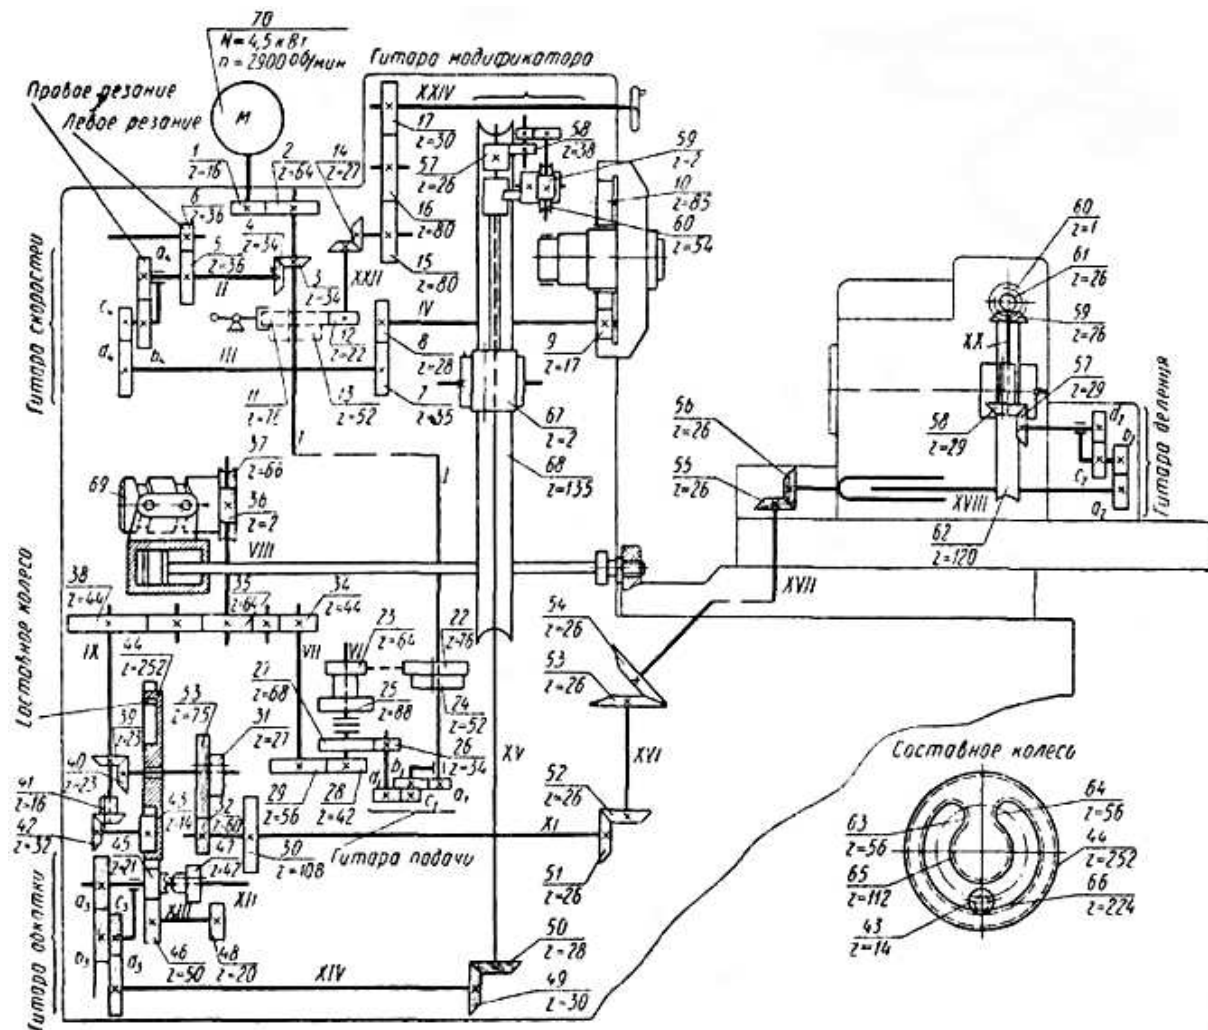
Станок для нарезания конических колес с дугowymi зубьями
